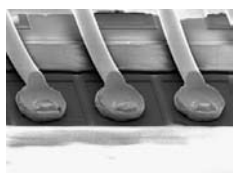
Сварка BSB (Ball Stitch on Ball)
